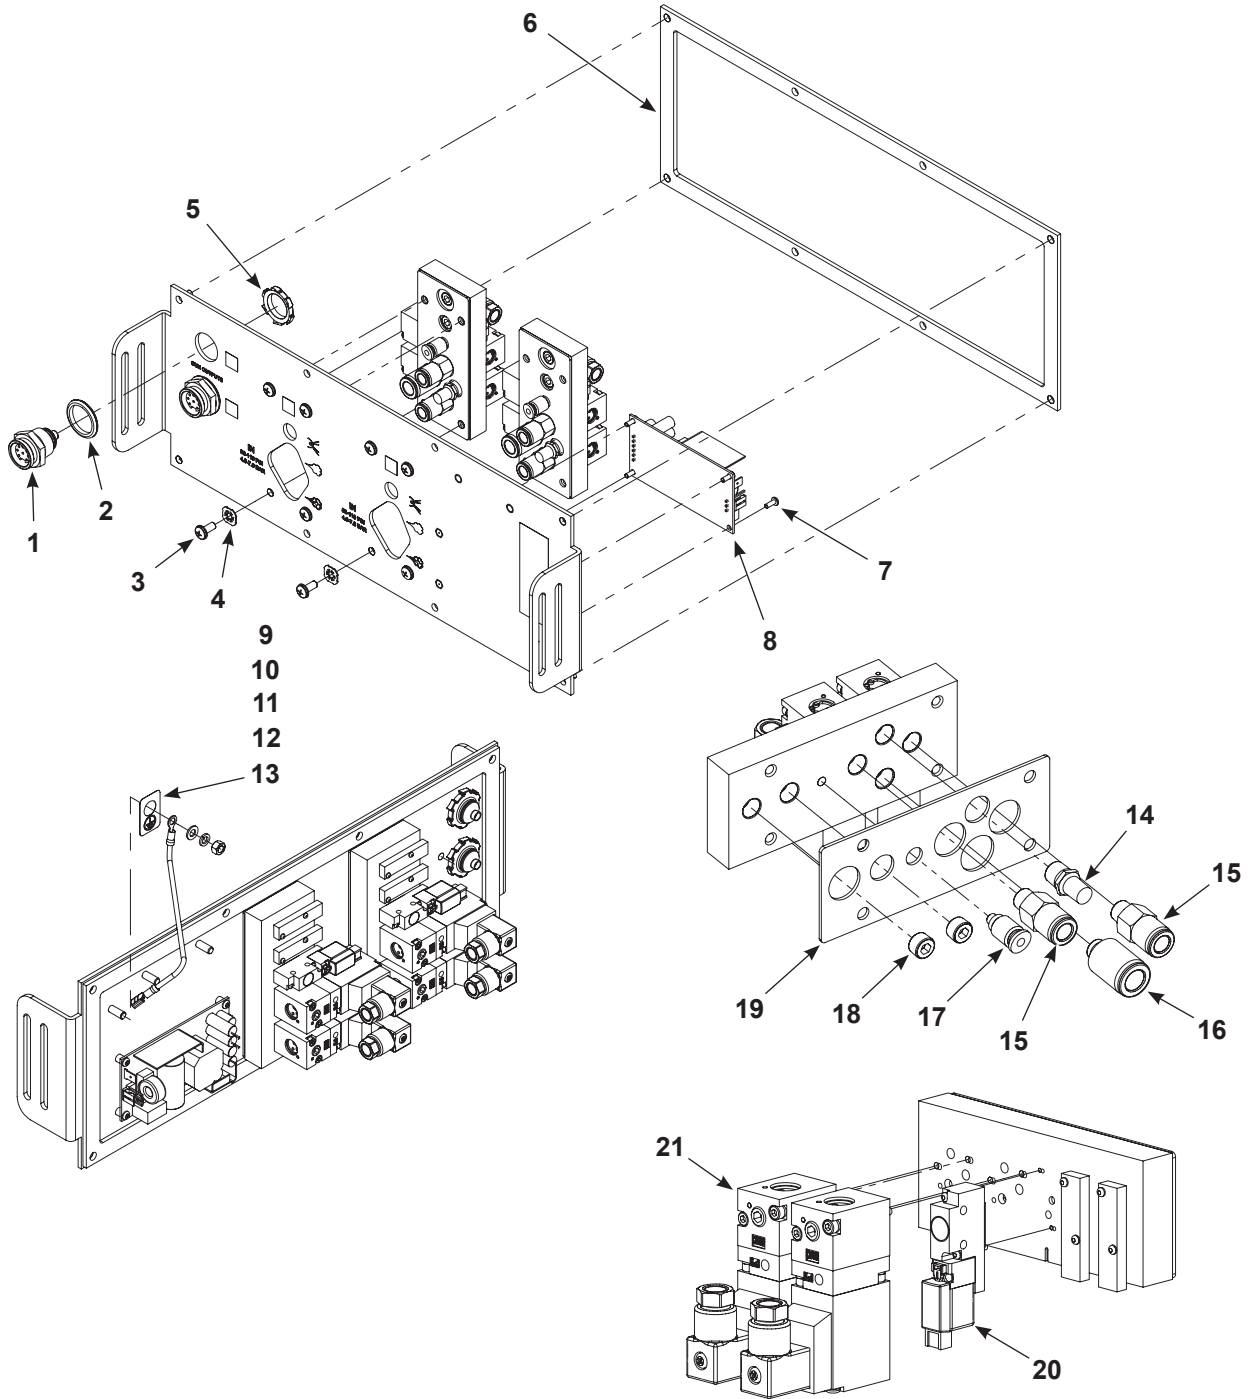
Pièces du sous-ensemble panneau arrière – contrôleurs pour deux et plusieurs pistolets
